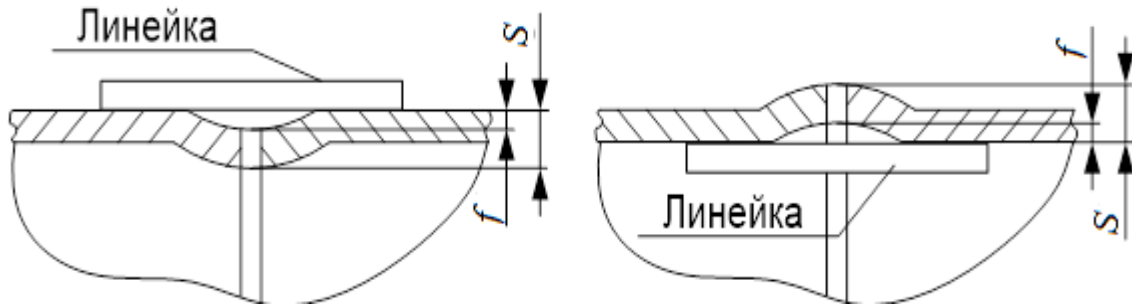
Контроль увода кромок продольных и кольцевых сварных соединений
